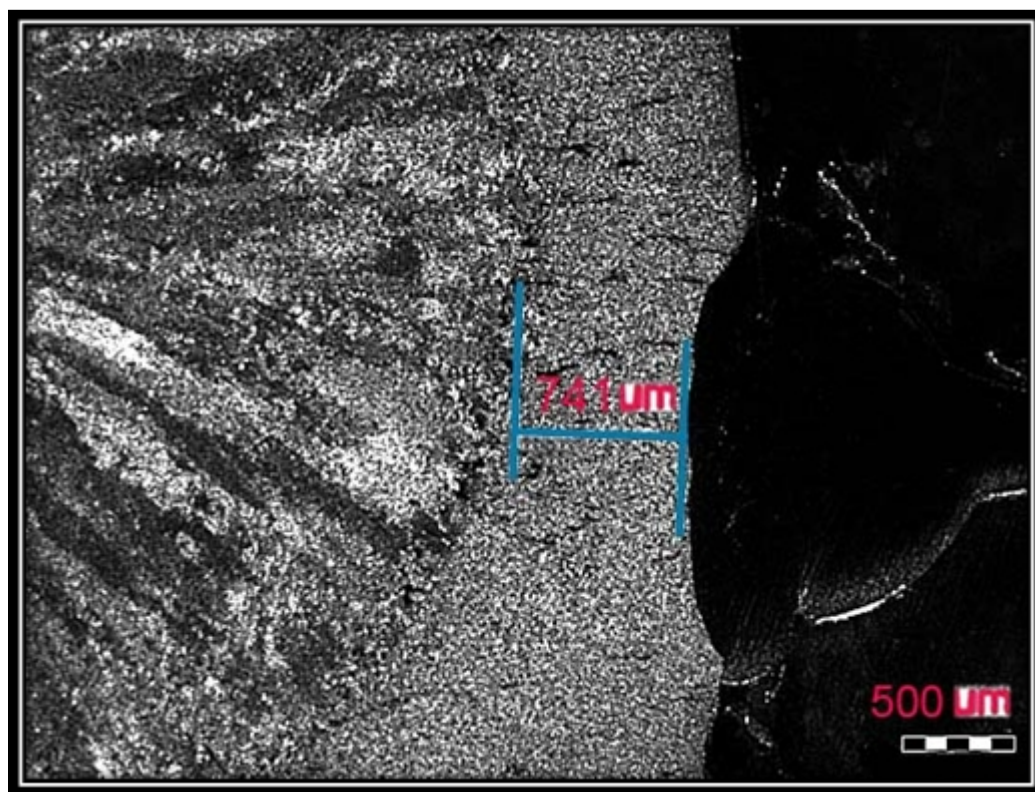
Makrostruktura vzorku 4.2 svařovaného elektrodou ϕ 2,5 mm – termočlánek č. T2
